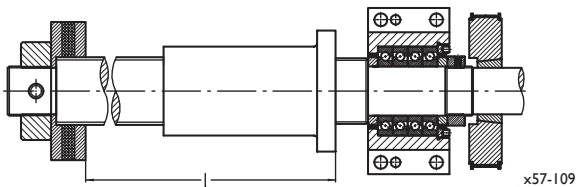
Kugelgewindetrieb mit fester Einspannung – Gegenseite frei
